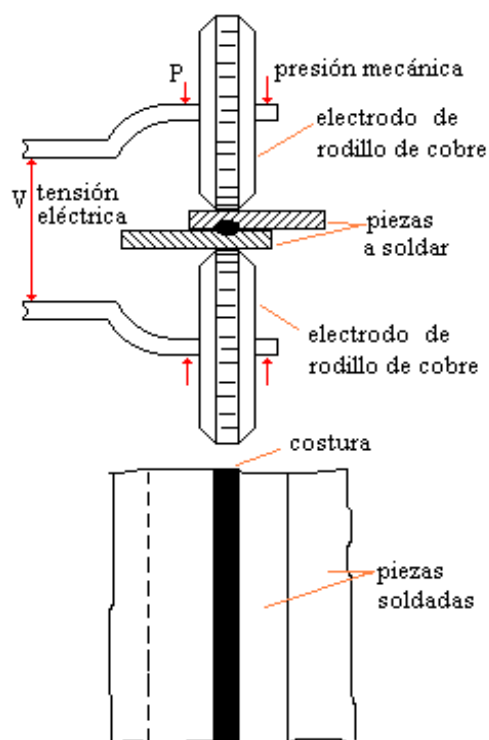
Circuito de soldadura por resistencia de costura RSEW
